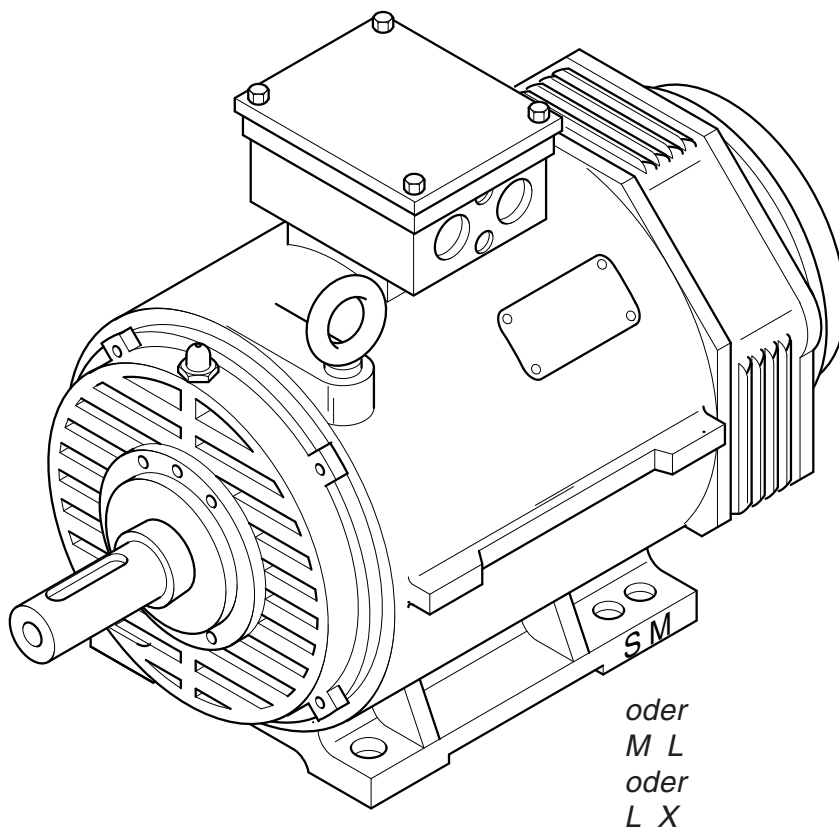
Fußbefestigungslöcher S,M oder M,L oder L,X
